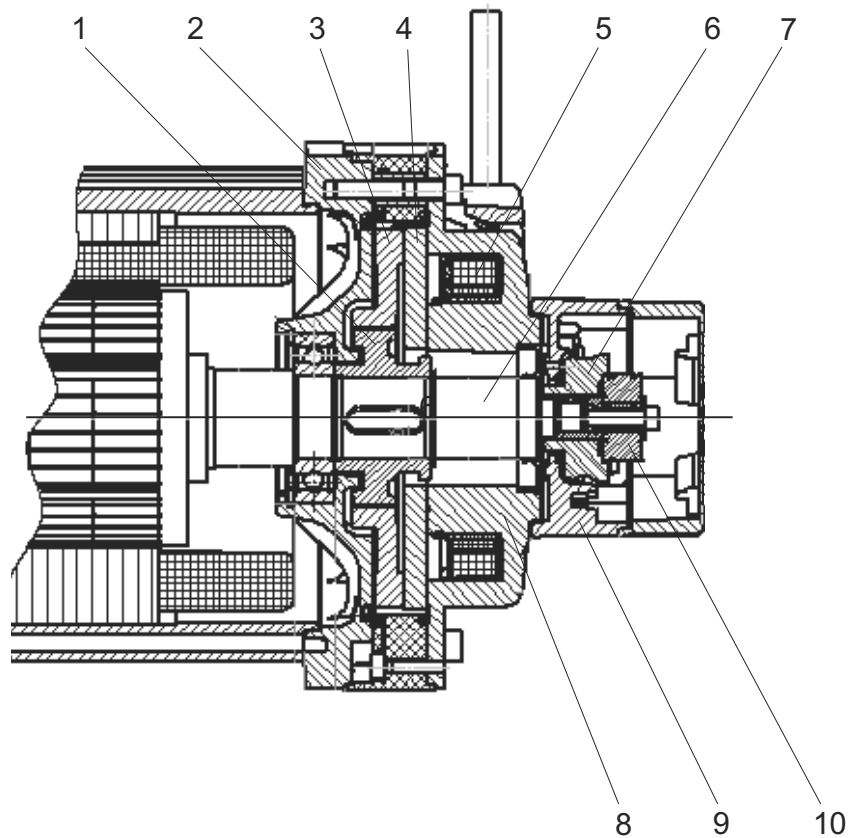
Prinzipieller Aufbau der Bremse mit Resolver RH1L
